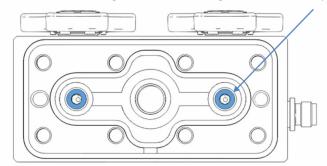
Pumpenkopf mit installierten Kolbendichtungen und Stützringen
